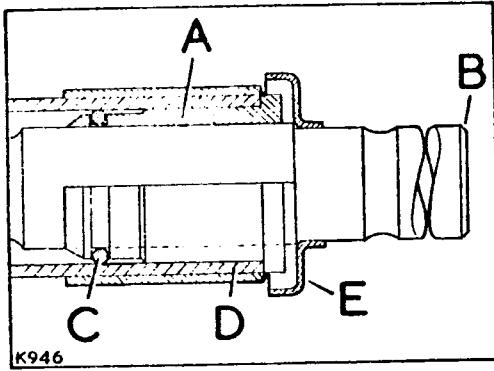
Sección longitudinal de la parte superior de la columna de tipo antiguo.
